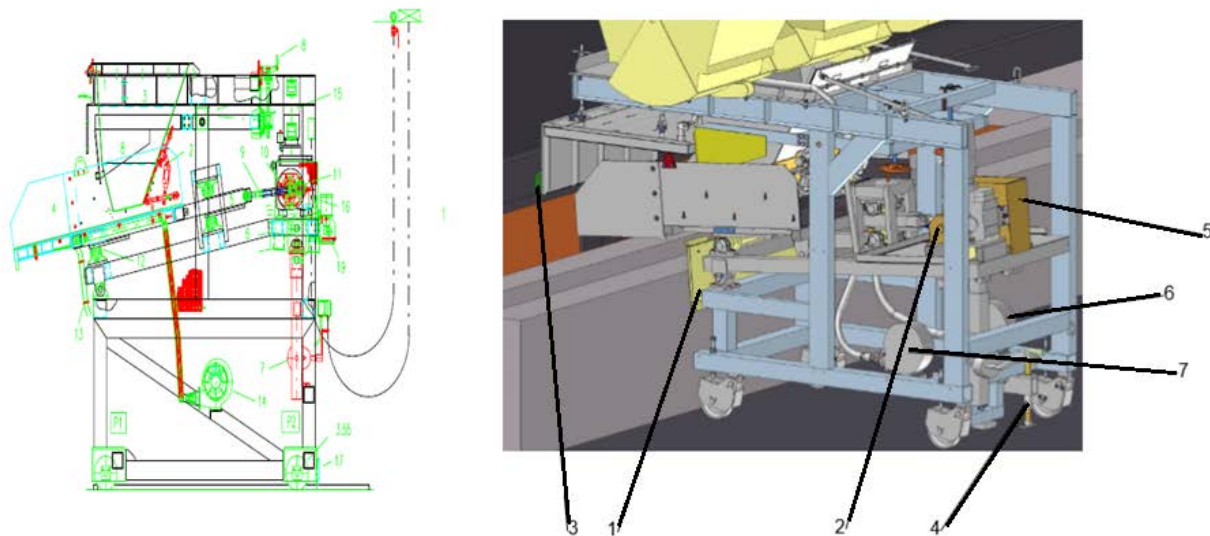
5 : Vue latérale de la machine (l'enfourneuse) ©MFG
